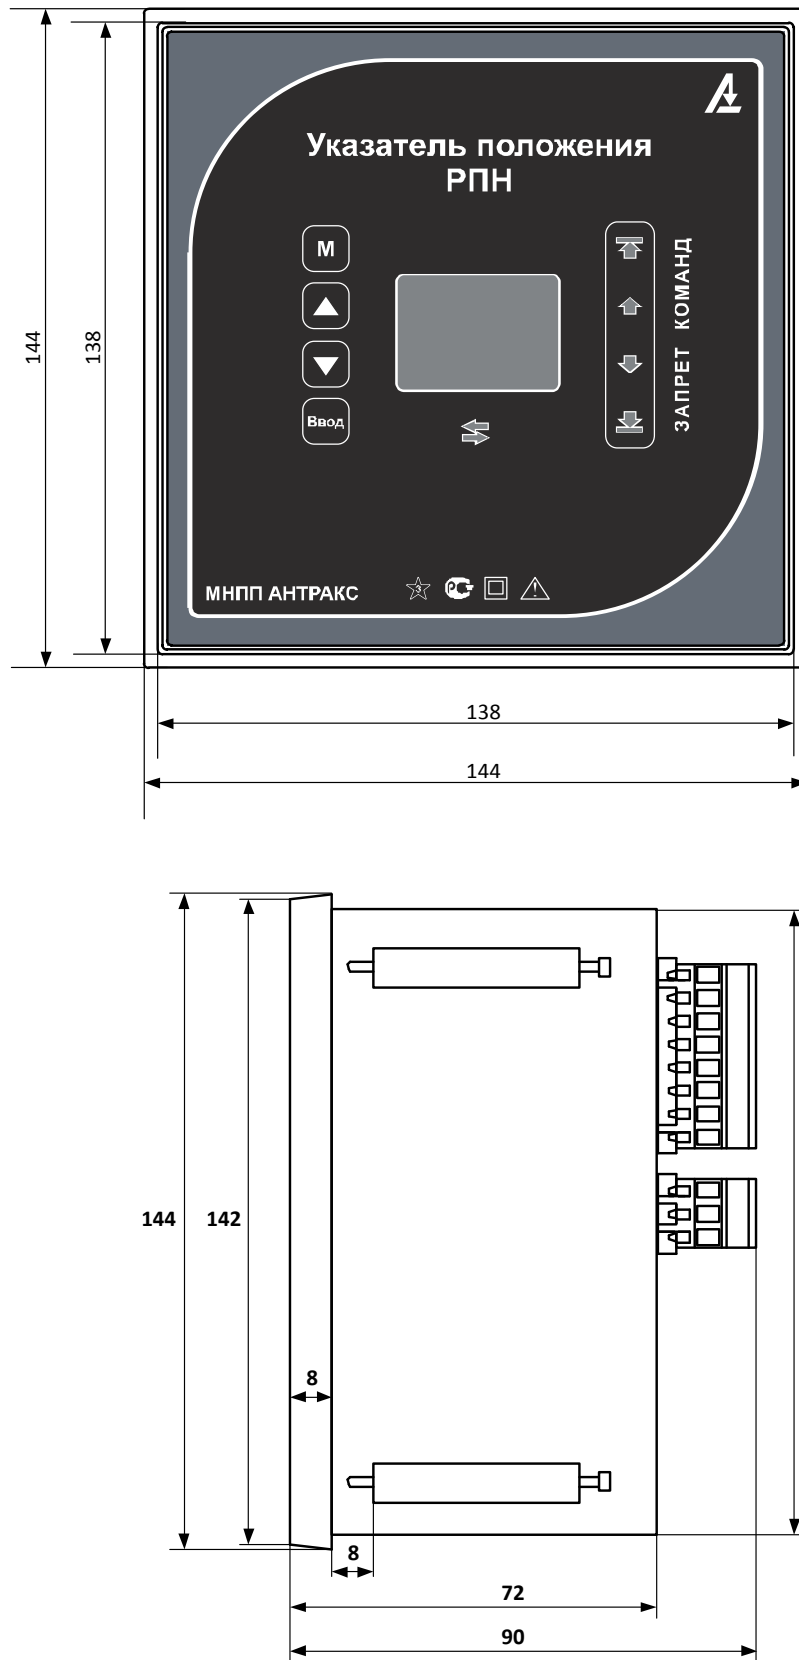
Габаритные размеры щитового варианта указателя положения РПН
